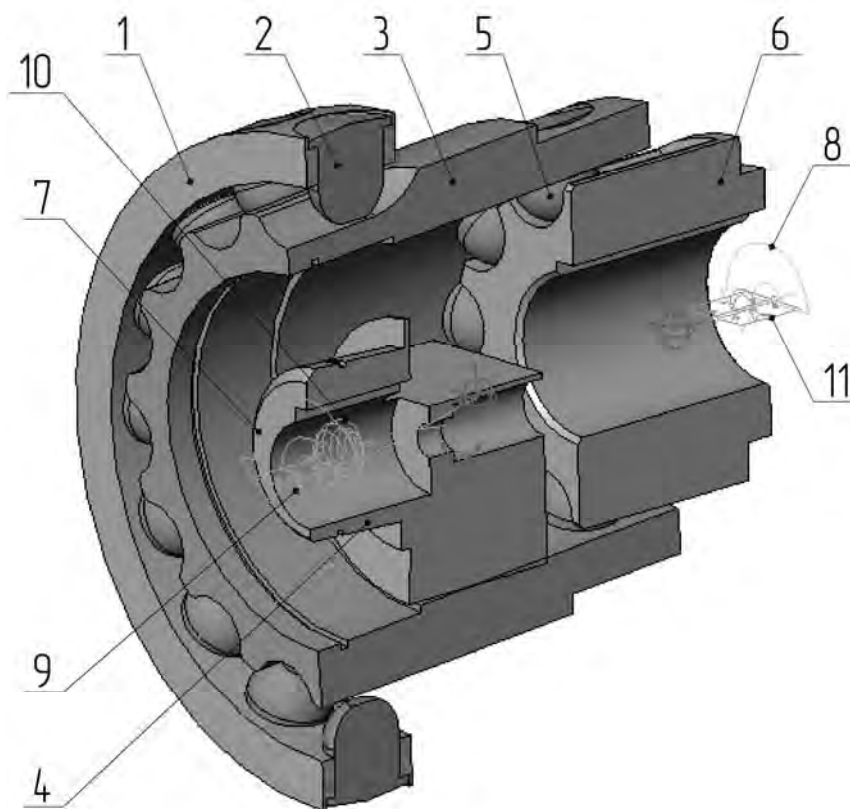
Компьютерная модель прецессионного редуцирующего механизма: 1 – корпус; 2, 5 – сферический палец; 3 – спутник; 4 – кривошип; 6 – угловая муфта; 7 – крутящий момент; 8 – нагружающий момент; 9 – подшипник входного вала; 10 – сферический подшипник; 11 – подшипник выходного вала
